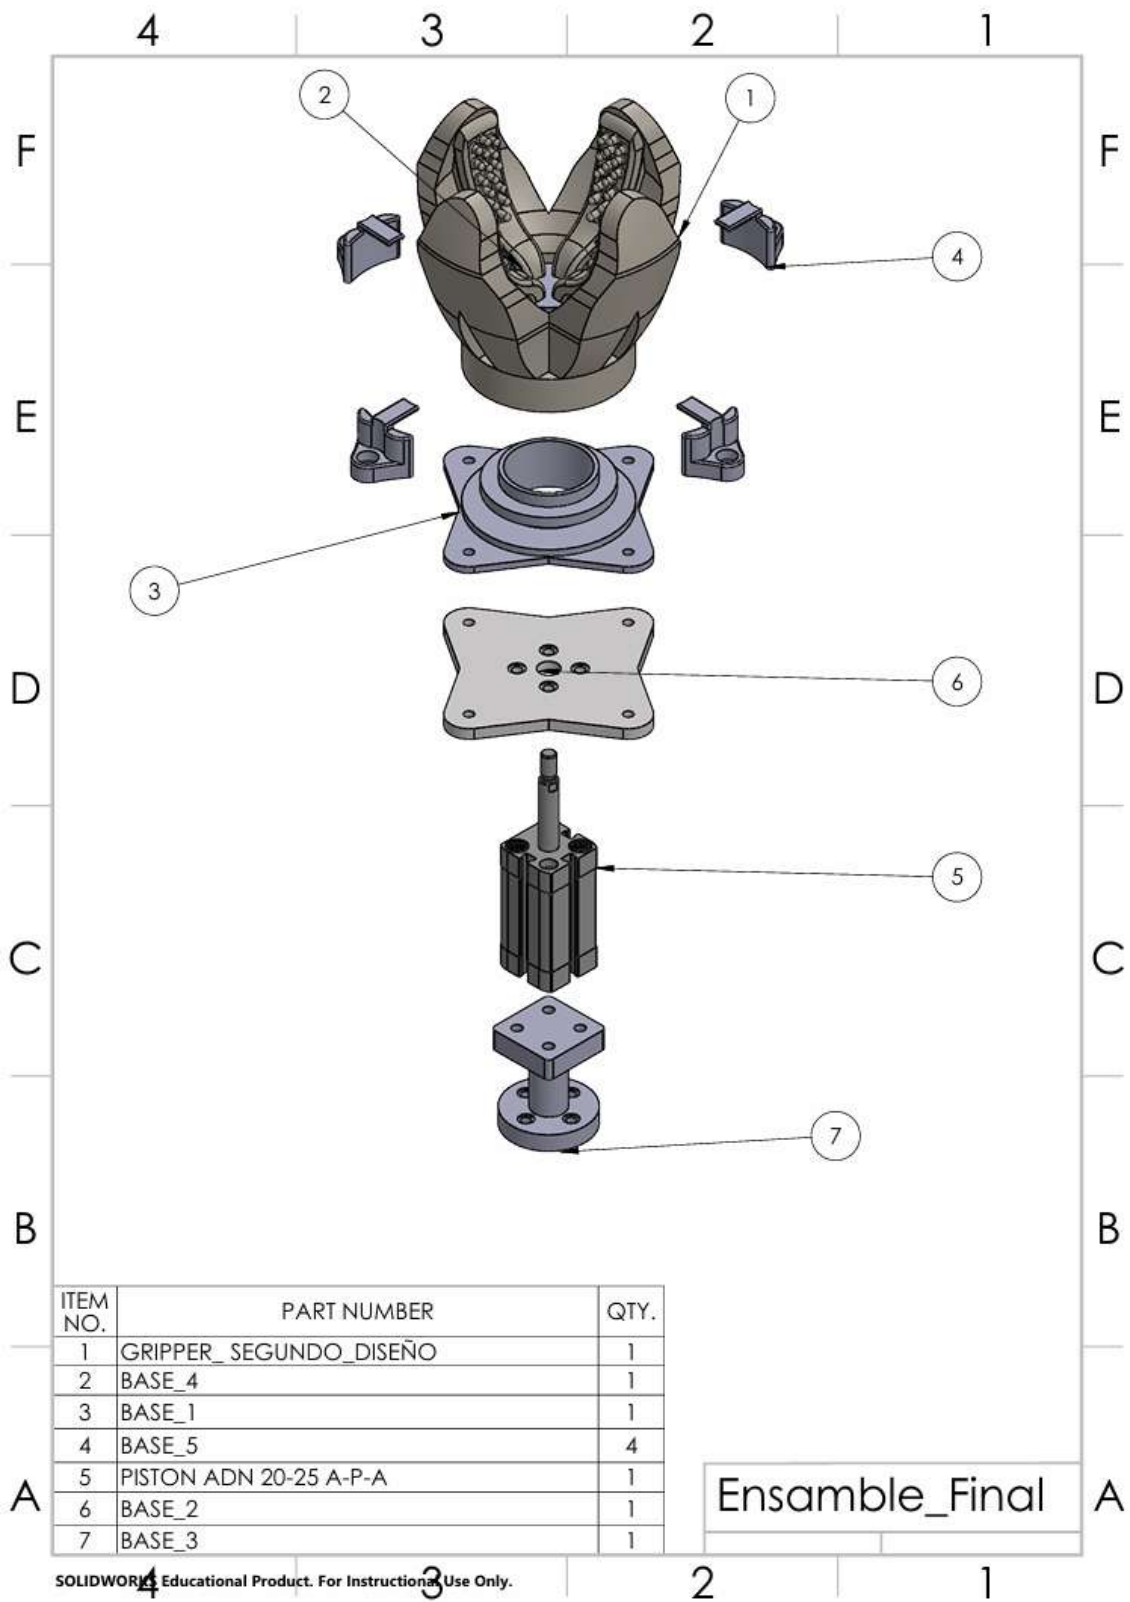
Vista explosionada del ensamble final del gripper, por J. Tumbaco, SolidWorks
